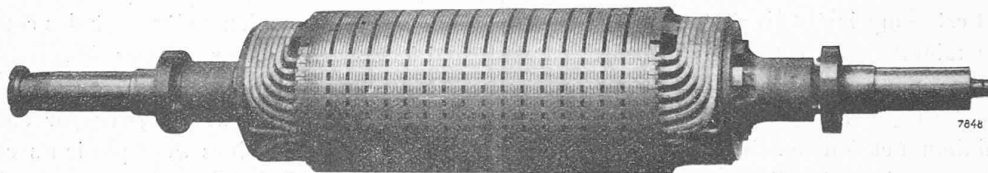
Rotor d'un turbo-alternateur, 3 000 t/m.
